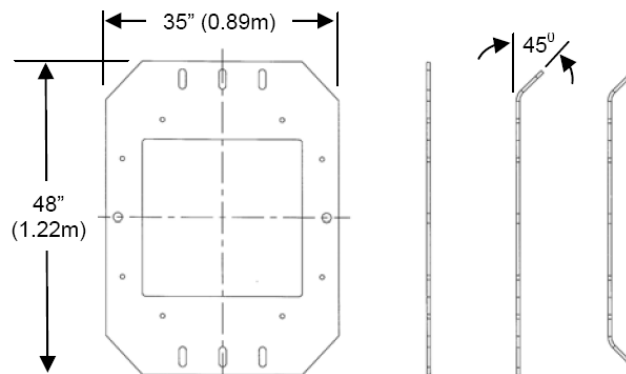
Accesorio adaptador para aislador tipo poste (cantiliever)
